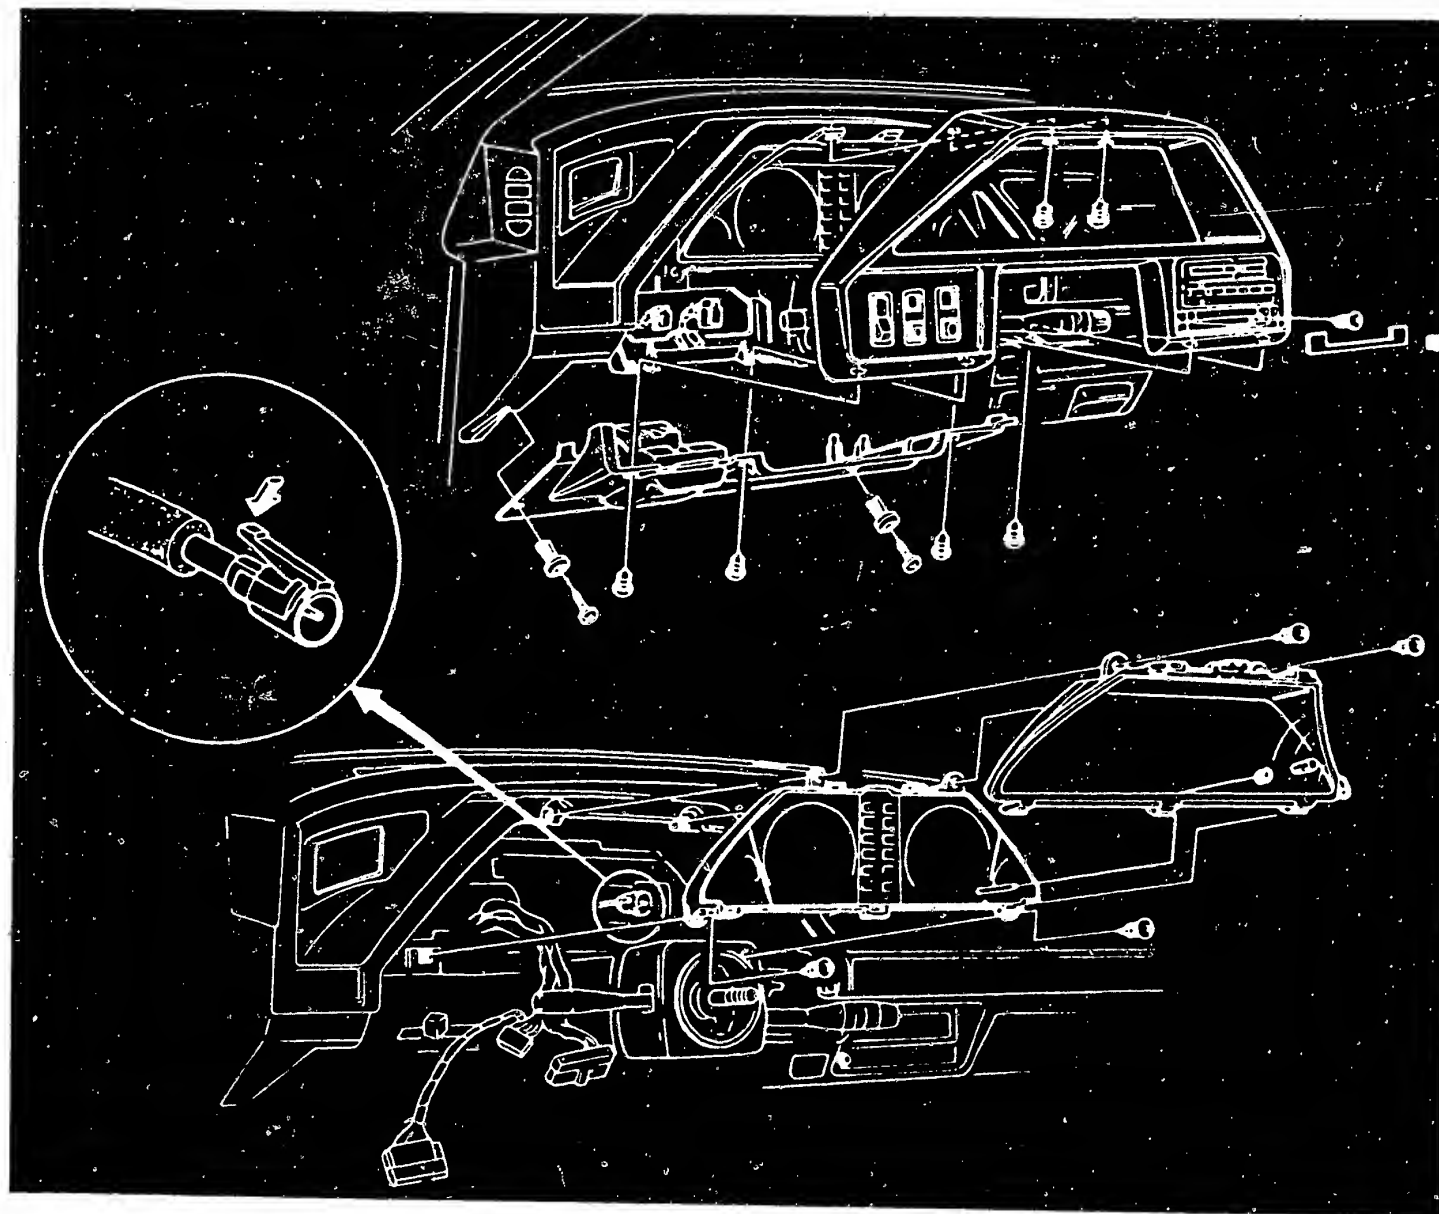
Das Bild zeigt die zur Demontage des Kombiinstrumentes zu lösenden Schrauben.
